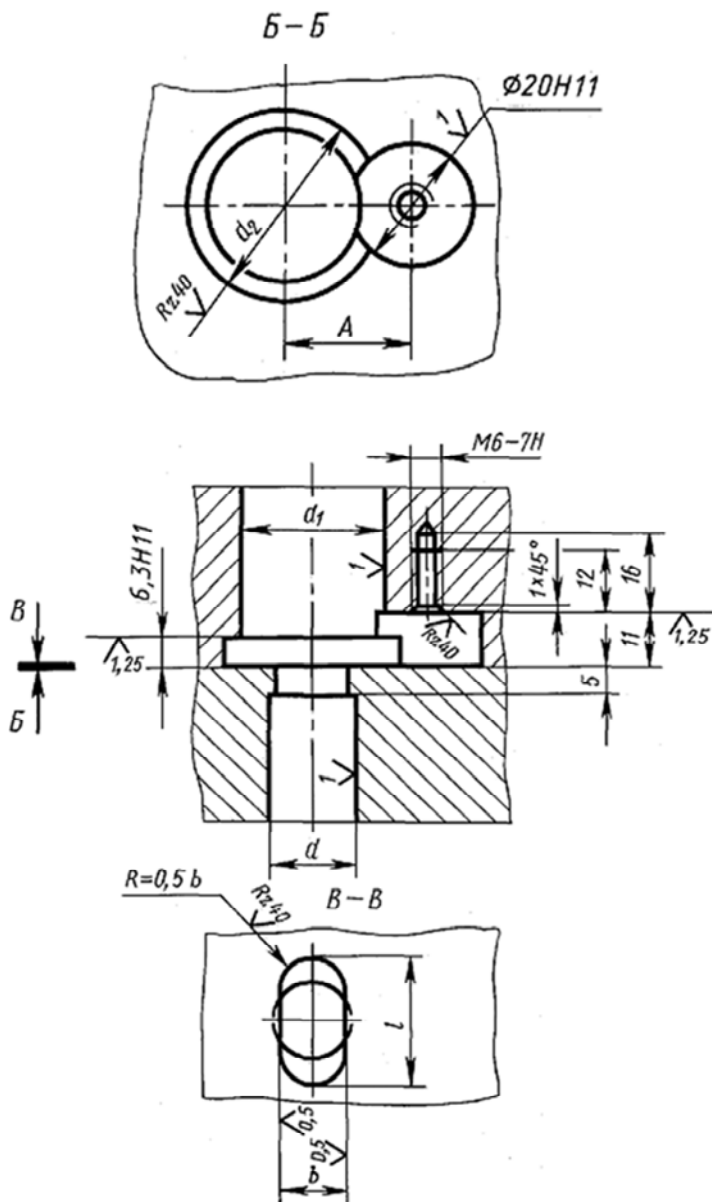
Конструкция гнезд для установки центрирующих соединений с зажимом
